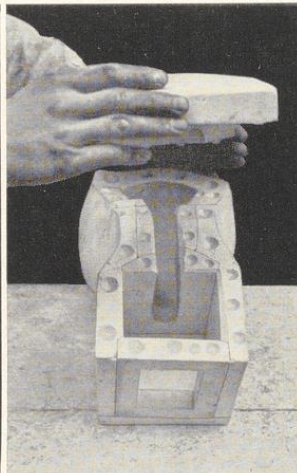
Die zusammengesetzte Form mit dem noch abgehobenen Schlußstück
